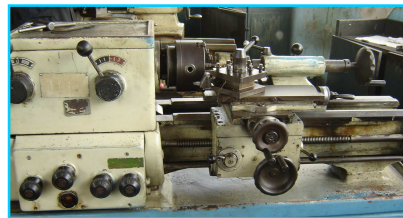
Maquina torneadora para paralelizar las partes distales del
